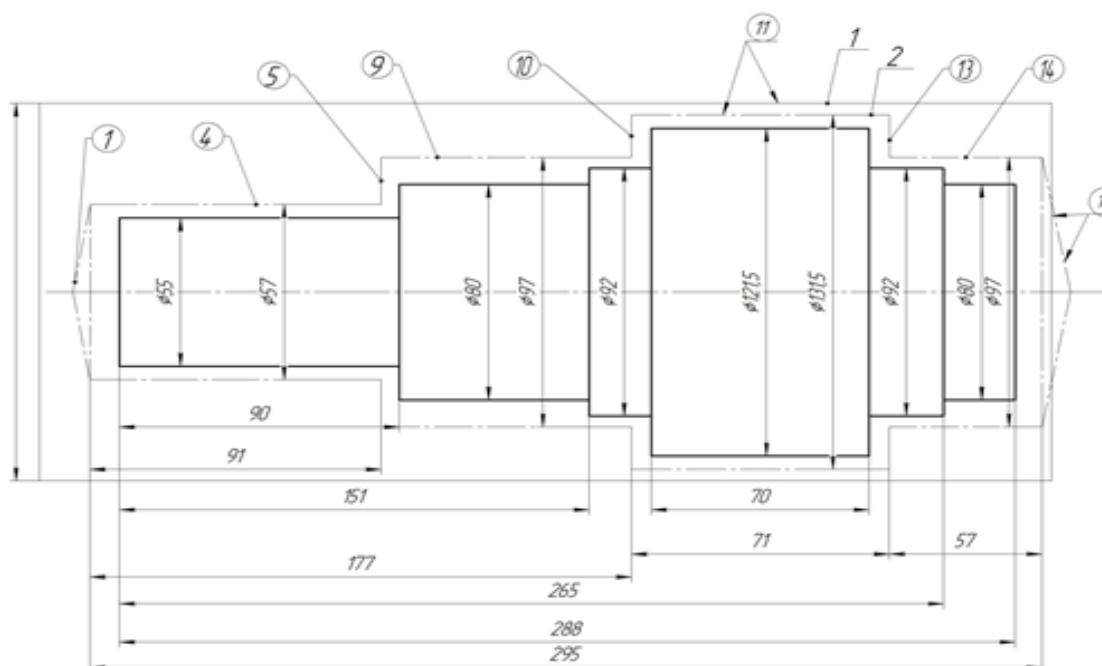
Заготовка 1-прокат,2-штамповка
